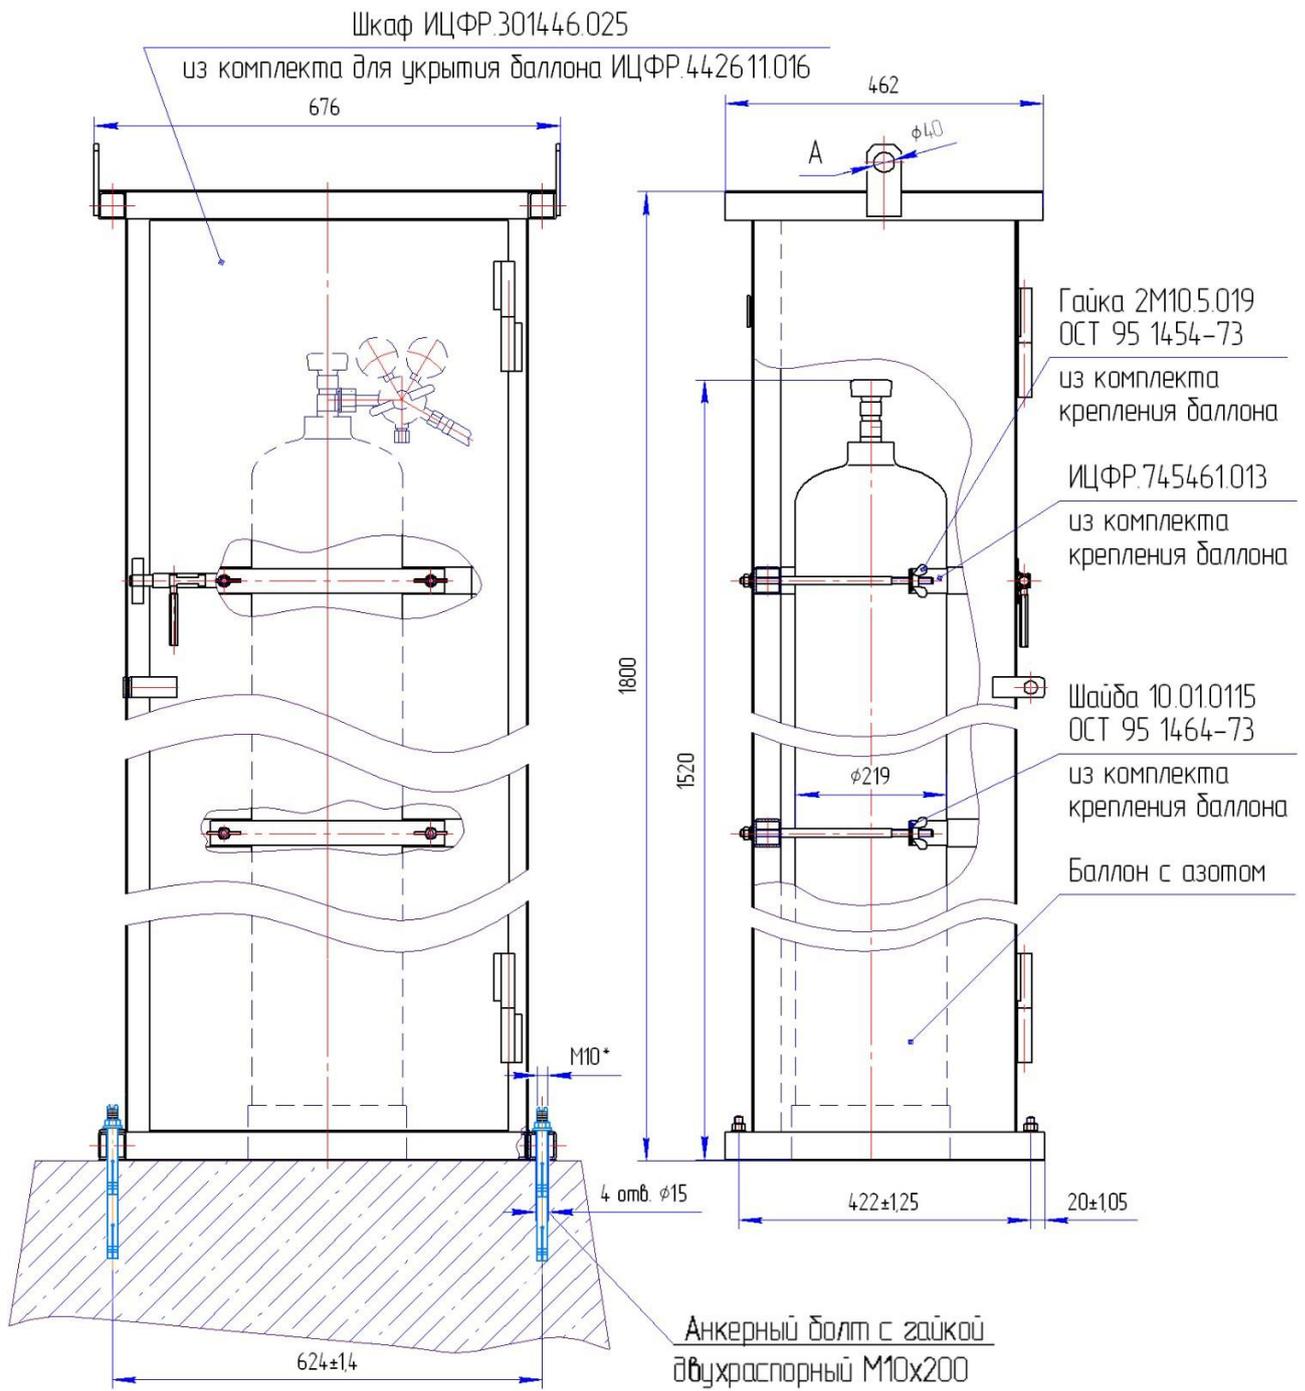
Габаритные и присоединительные размеры шкафа ИЦФР301446.025
